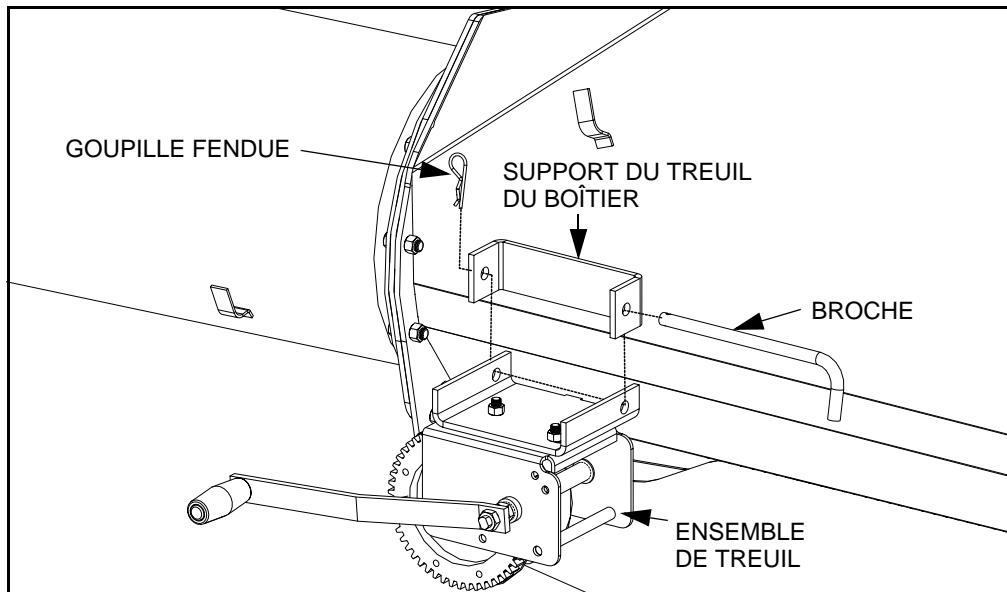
Installation du treuil sur l'autre côté du boîtier
